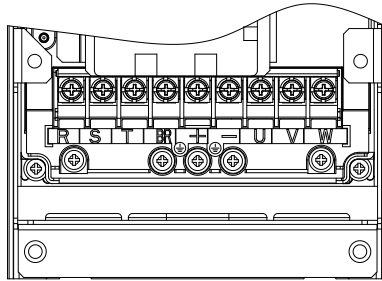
Расположение клемм главной цепи конструкций T2 - T4
